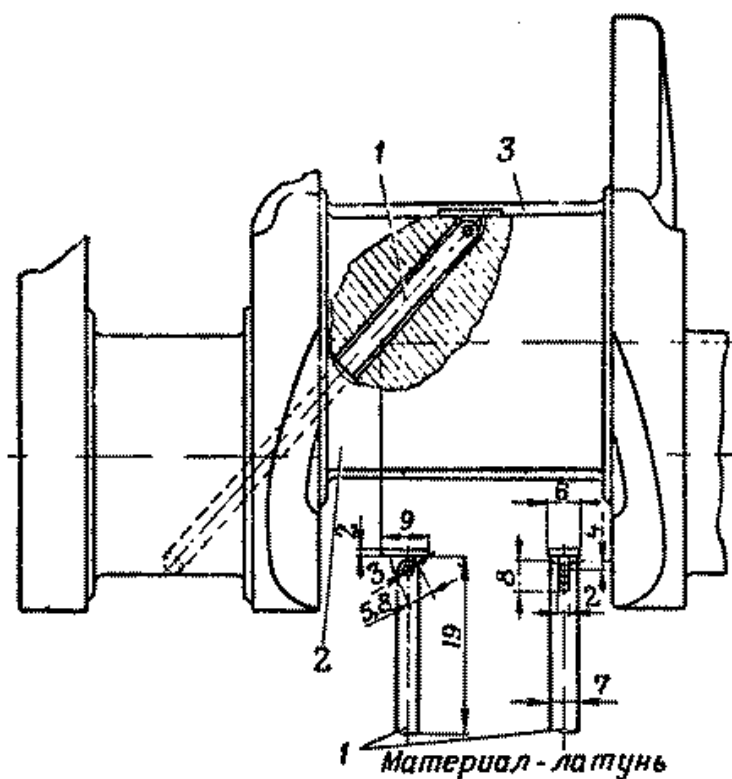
Установка пальца для снятия верхних вкладышей коренных подшипников:
